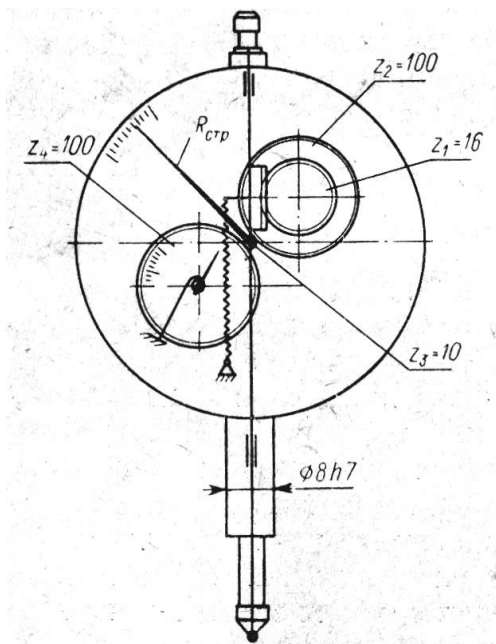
Схема реечно-зубчатой измерительной головки типа ИЧ
